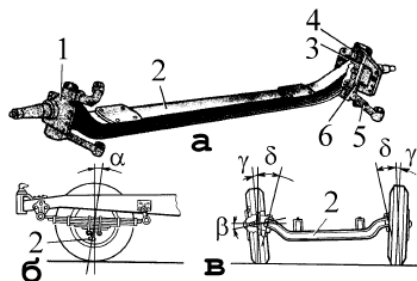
Передняя ось автомобиля: а – устройство; б – схема продольно- го наклона шкворня; в – схема по- перечного наклона шкворня; 1 – поворотная цапфа; 2 – двутавровая балка; 3 – шкворень; 4 – масленка; 5 – поворотный рычаг; 6 – опорный подшипник; α – угол продольного наклона шкворня; β – угол наклона оси цапфы; γ – угол развала колес; δ – угол поперечного наклона шкворня
